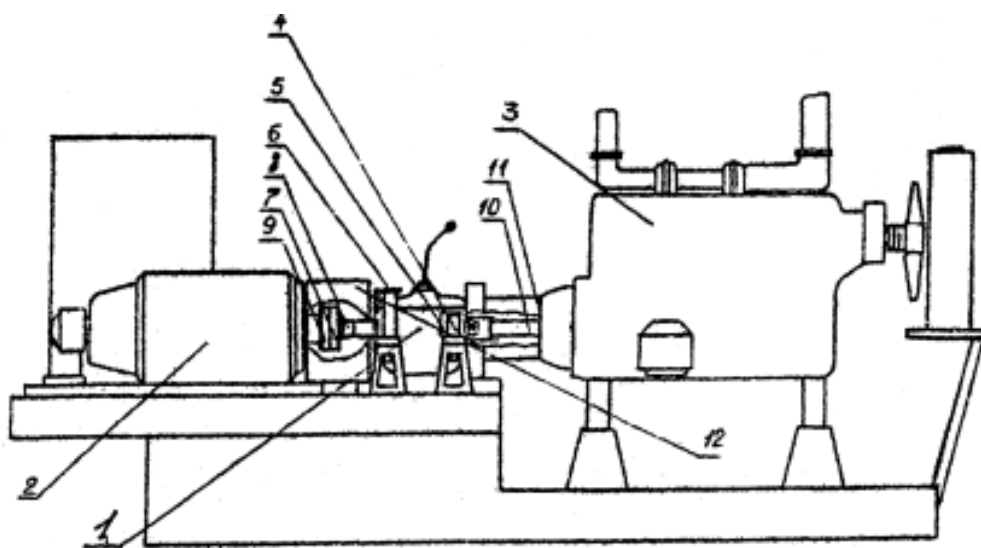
Стенд для обкатки двигателей с мультипликатором:
